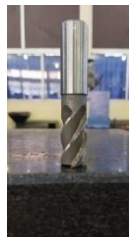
Sudut 5° *End Mill Grinding Attachment
